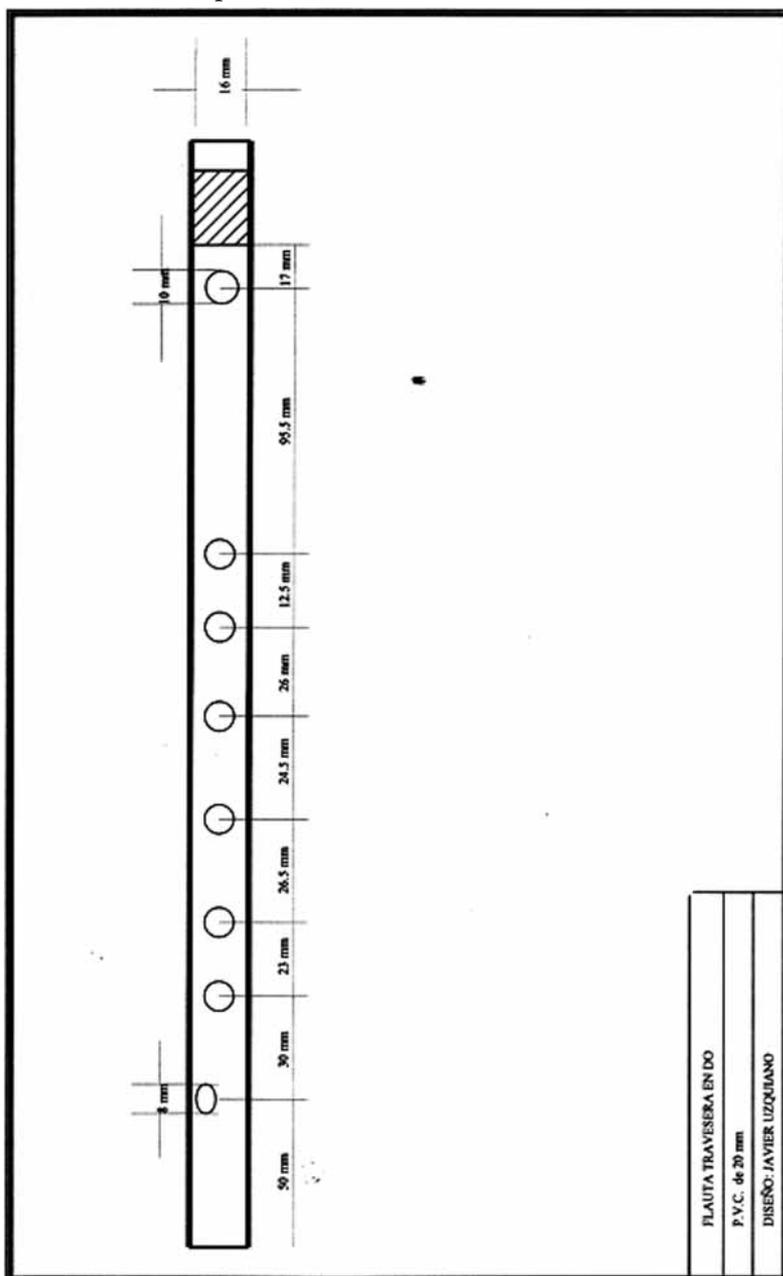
Plano para la construcción de una flauta travesera
